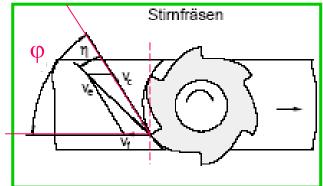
Stirnfräsen / Frezare frontală [SCH 18]
